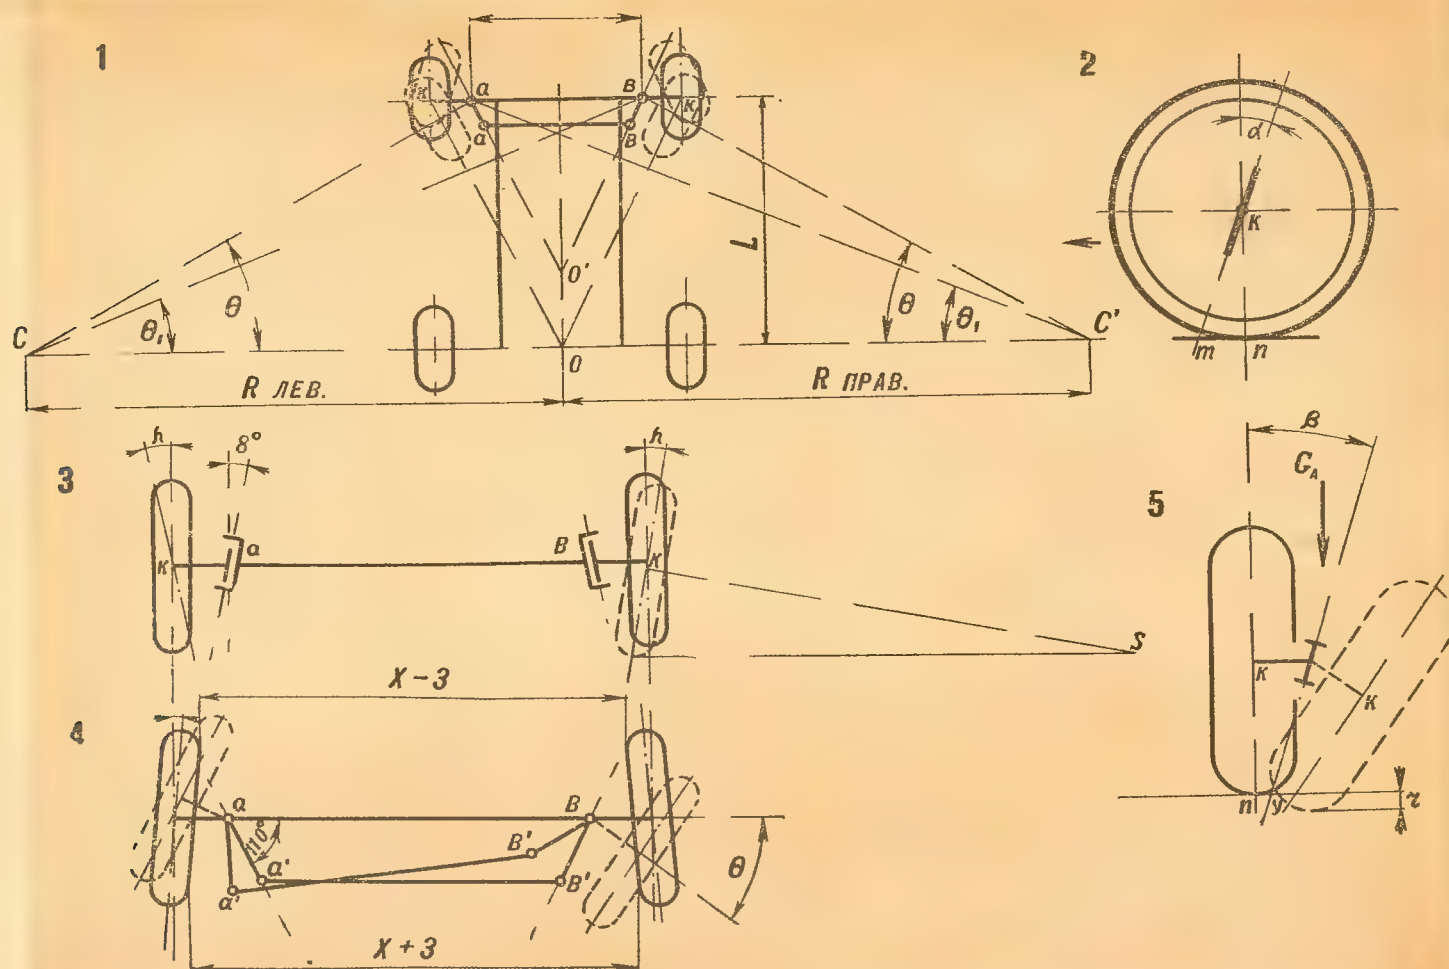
Установочные углы управляемых колес и кинематика рулевого привода:
